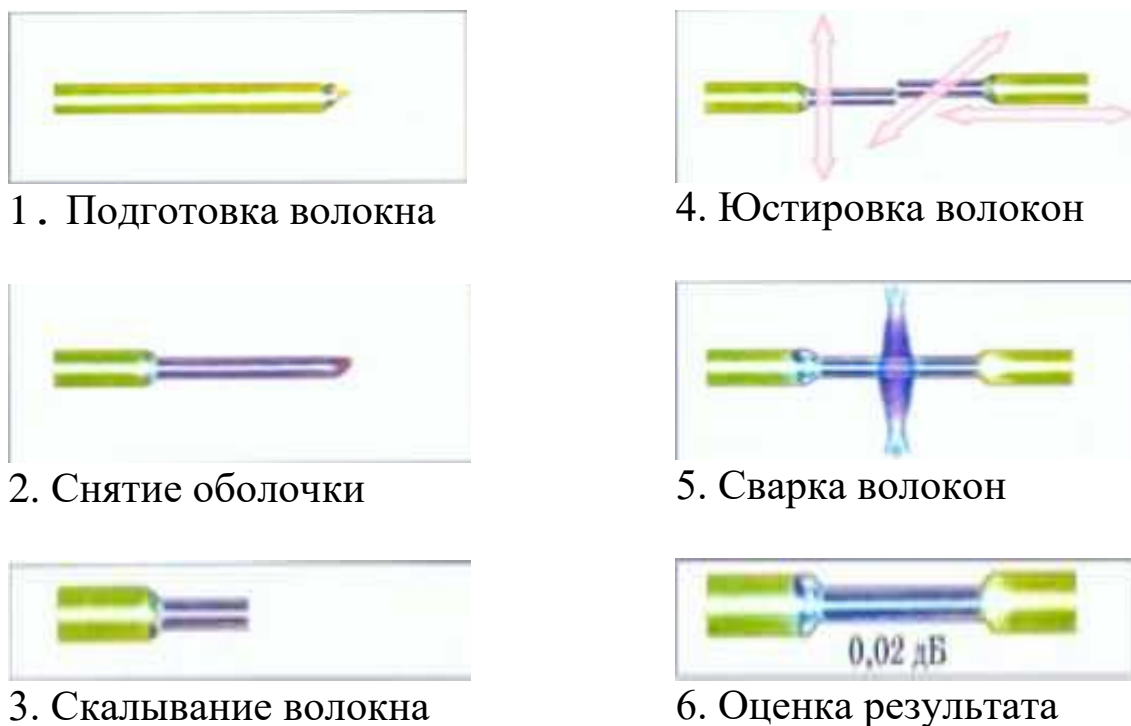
Операции подготовки и сварки оптического волокна
